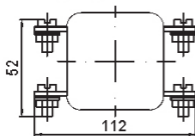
Габаритные, установочные, присоединительные размеры кулачковых переключателей 4G10, 4G16, 4G25 закрытого исполнения
